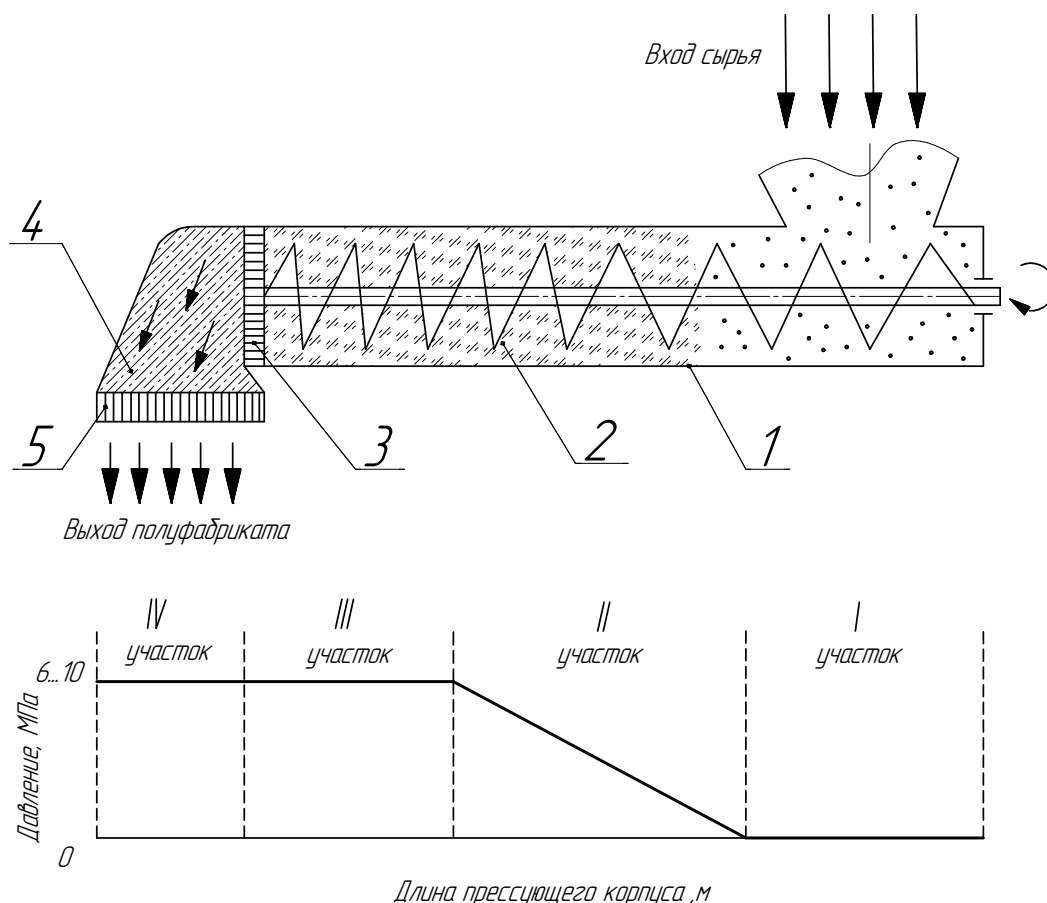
Схема прессующего корпуса макаронного пересса: 1 – корпус; 2 – шнек; 3 – перфорированная решетка; 4 – предматричная камера; 5 – матрица
